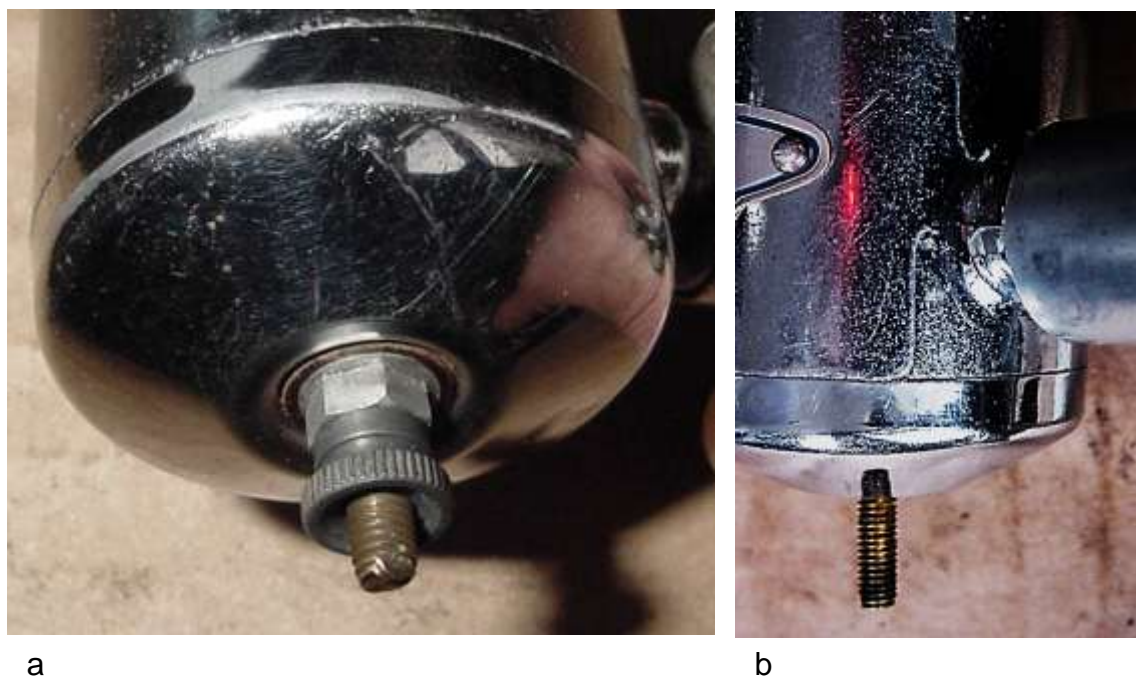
Gehäusedetails: a) Boden, b) Eingegossener Drehbolzen
